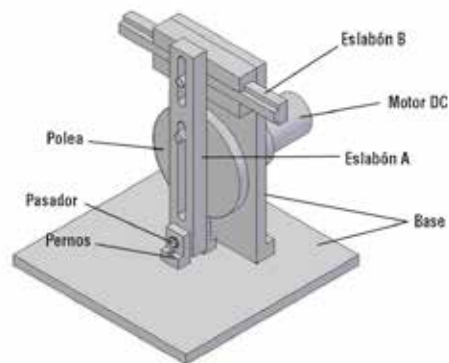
Diseño mecánico. Fuente: elaboración propia.
